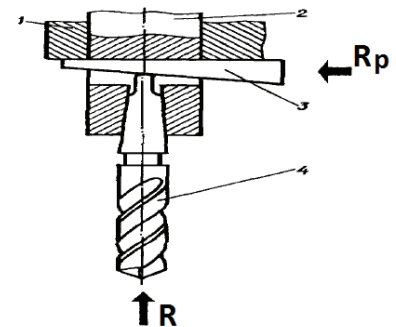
Закріплення інструменту в шпинделі свердлувального верстата
